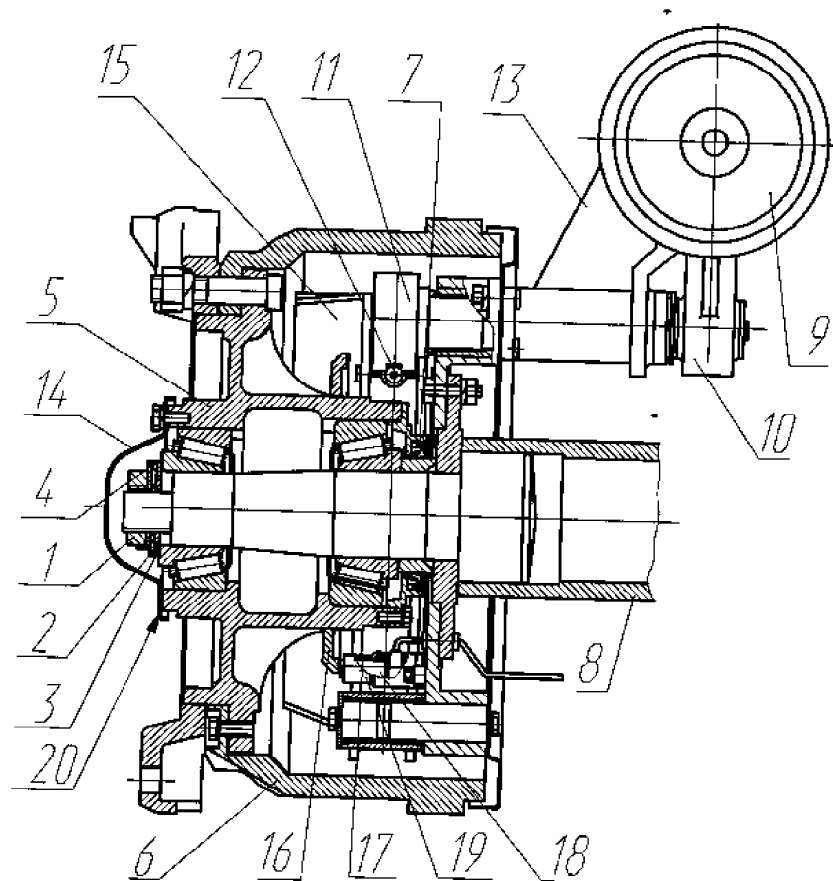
Ось с тормозными механизмами 420х160 прицепа МАЗ-856100
